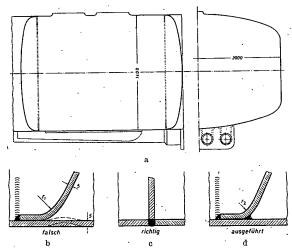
Schweißnahtausführung an Treibstofftanks aus Aluminium 99,5 a Gesamtanordnung, b Falsche Ausführung, c Richtige Ausführung, d Ausgeführte Schweißung
